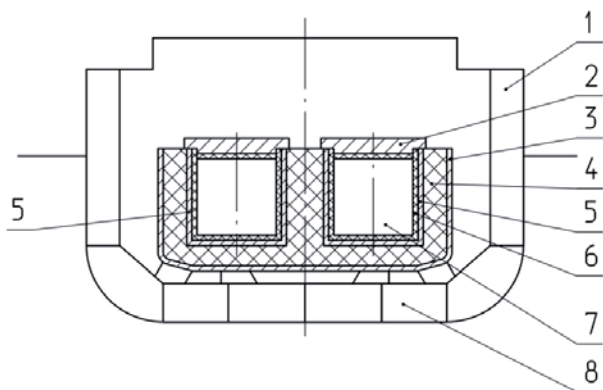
Схема расположения конструкции БЗ на плавучих сооружениях для перегрузки и хранения РАВ: 1 — двойной борт; 2 — крышка контейнера; 3 — внешний корпус конструкции БЗ; 4 — бетонный слой; 5 — баки для грузов; 6 — композиционный защитный слой; 7 — груз; 8 — двойное дно
